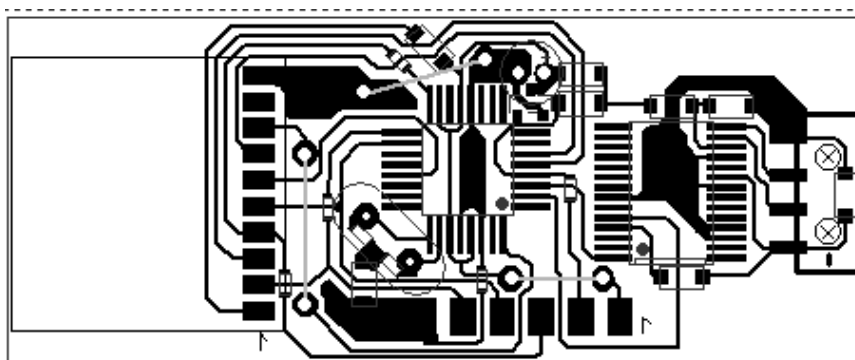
Вид друкованої плати USB-модуля в Sprint-Layout 5.0
